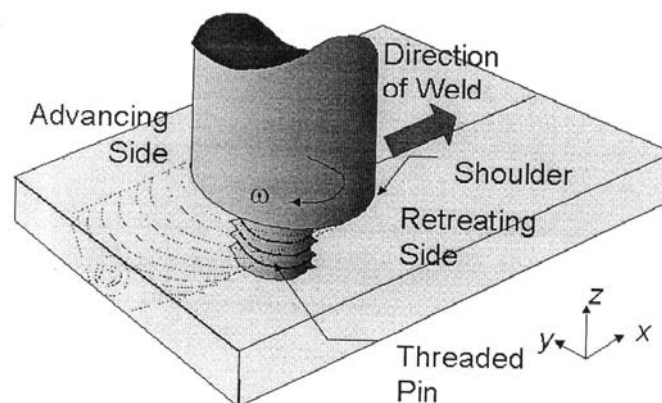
Schémas du procédé de soudage par friction malaxage (FSW) [Shercliff 2001]
